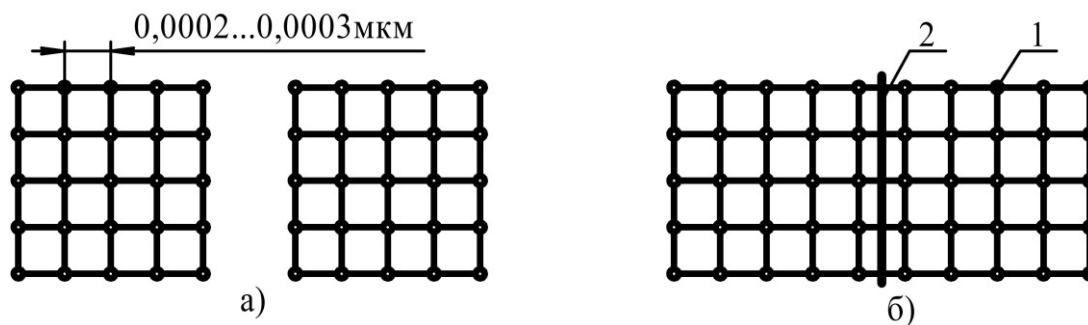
Схема утворення зварного з'єднання між двома монокристалами: а) – монокристали до зварювання; б) – монокристали після зварювання; 1 – іон кристалічної ґратки; 2 – границя зварного з'єднання
